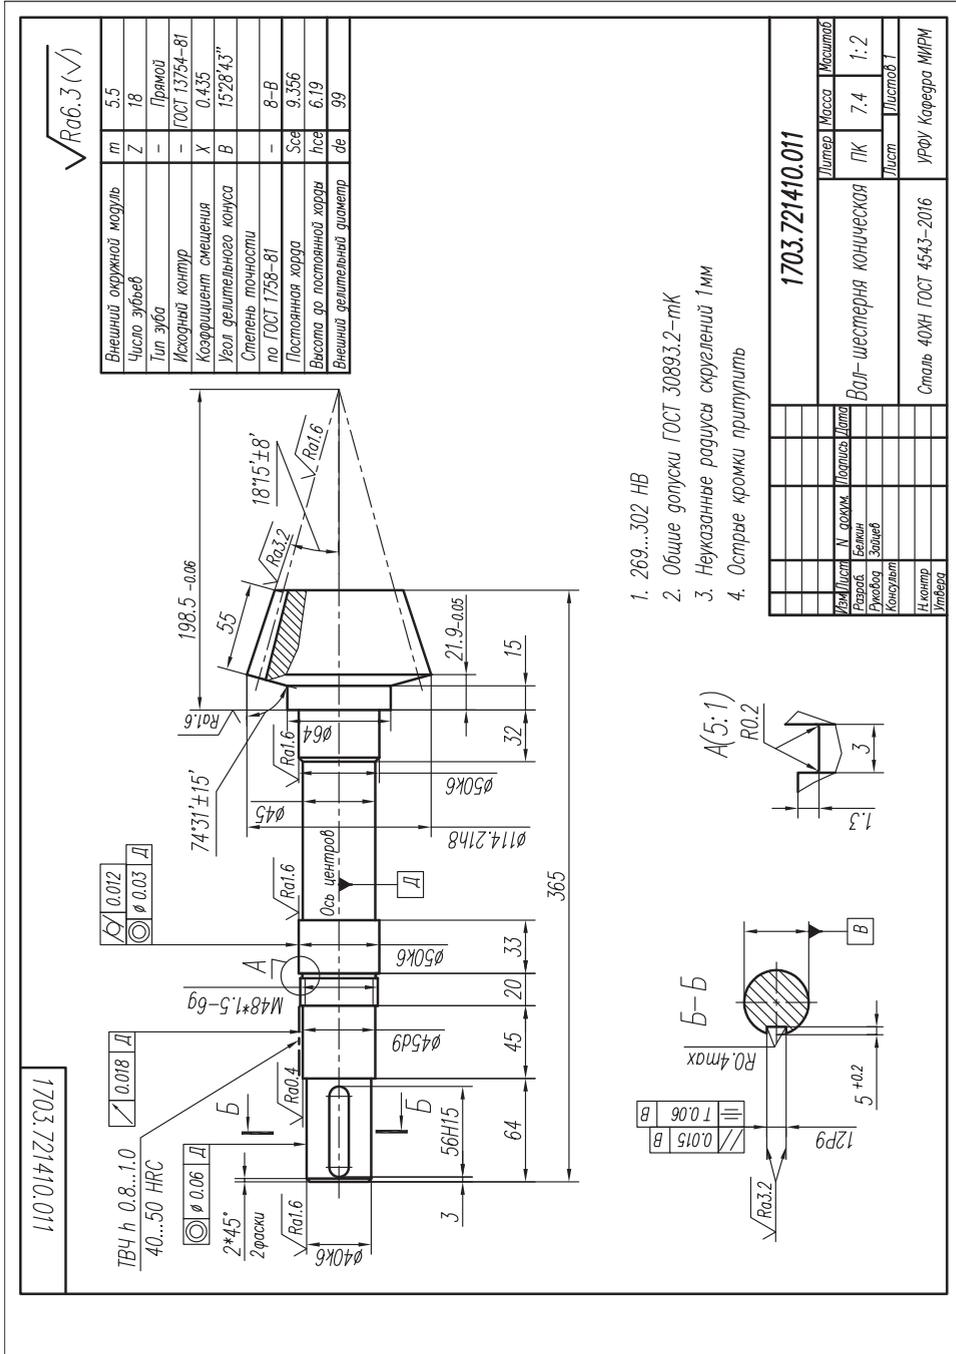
Рабочий чертеж вала-шестерни конической
